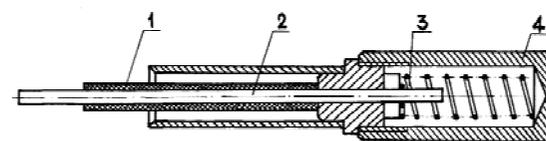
Приспособление для надевания вакуумной трубки:
